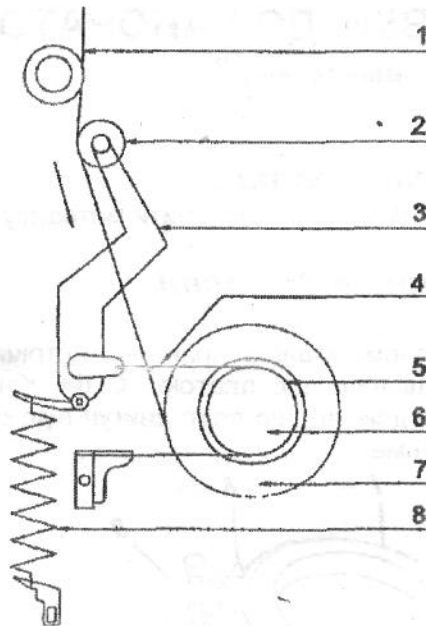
Механізм оберненого натягу: 1 - стрічка, 2 - стійка натягу, 3 - важіль натягу, 4 - металева стрічка, 5 - фетрова смужка, 6 - тормозний диск, 7 - приймальний вузол СПМ, 8 - пружина
